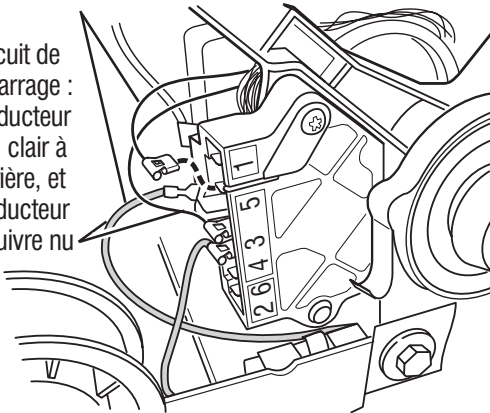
Points de mesure pour le bobinage du moteur (bobinage principal et bobinage de démarrage)
